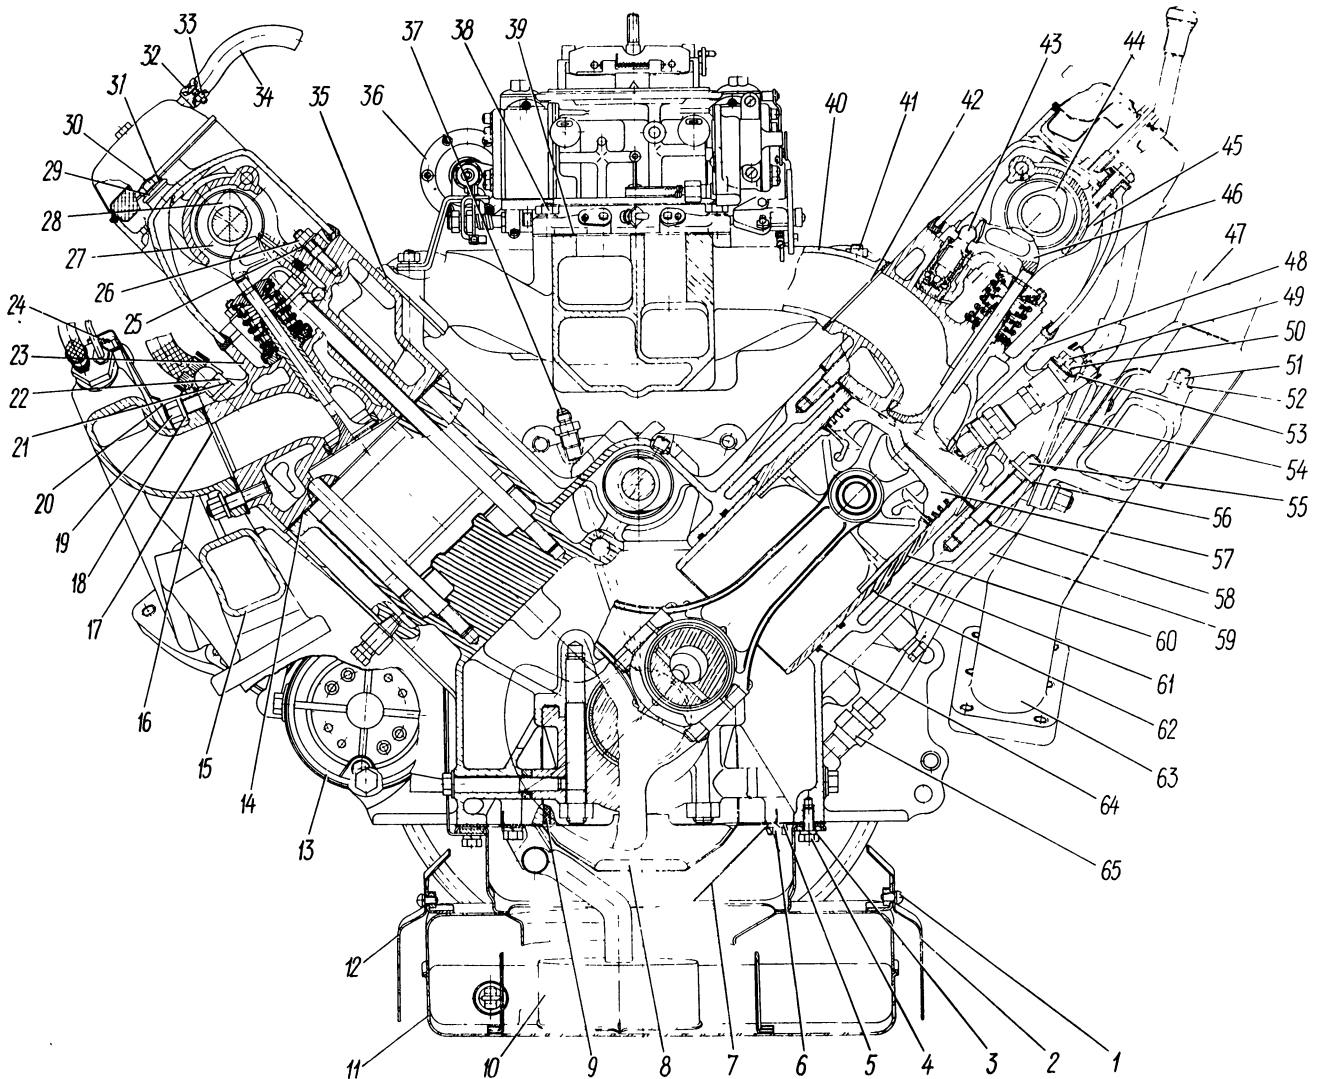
Двигатель ЗИЛ-4104 (поперечный разрез):
